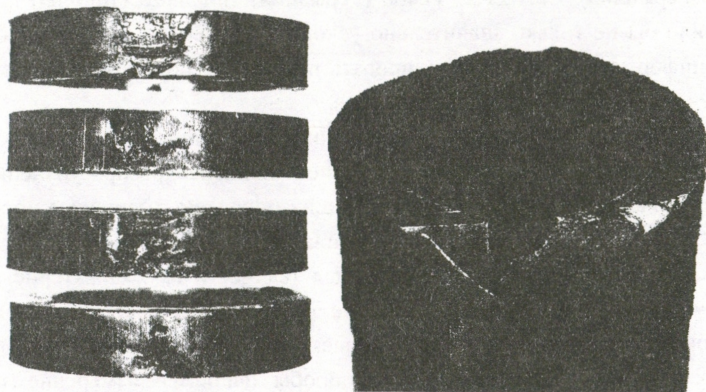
Сколы зуба блокирующего кольца синхронизатора коробки передач легкового автомобиля в процессе нарезки (*а*) и выкрашивание трубы в процессе прессования (сплав ЛМцАЖКС) (*б*)
